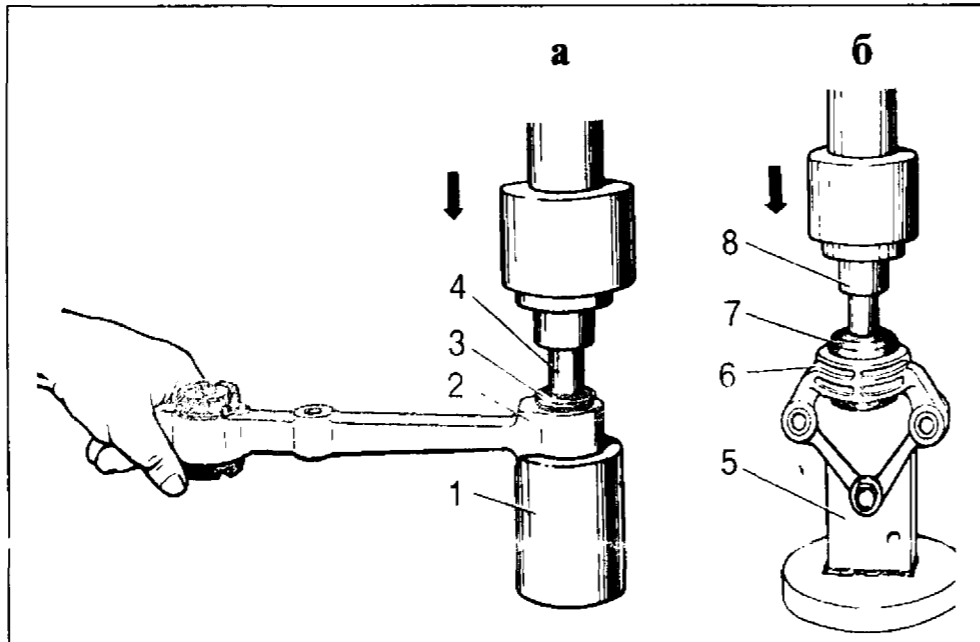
Выпрессовка резинометаллических шарниров из рычага подвески (а) и кронштейна крепления растяжки (б): 1 — втулка; 2 — рычаг подвески; 3 — резинометаллический шарнир; 4 — оправка; 5 — приспособление 67.7823.9540; 6 — кронштейн крепления растяжки; 7 — резинометаллический шарнир; 8 — оправка
